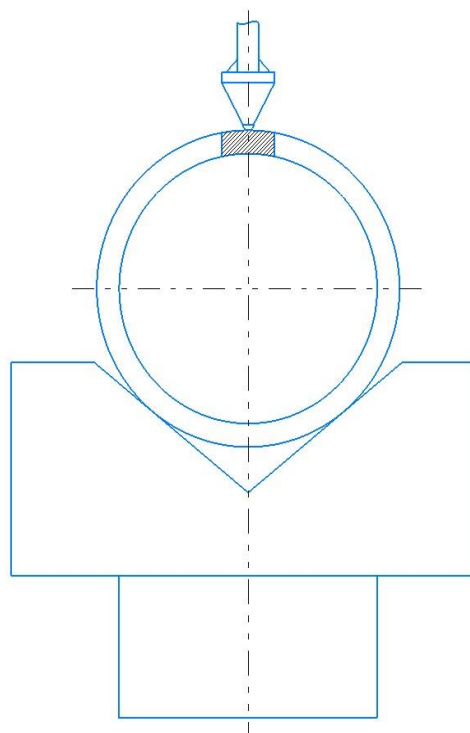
Измерение твердости сварочного шва трубы
